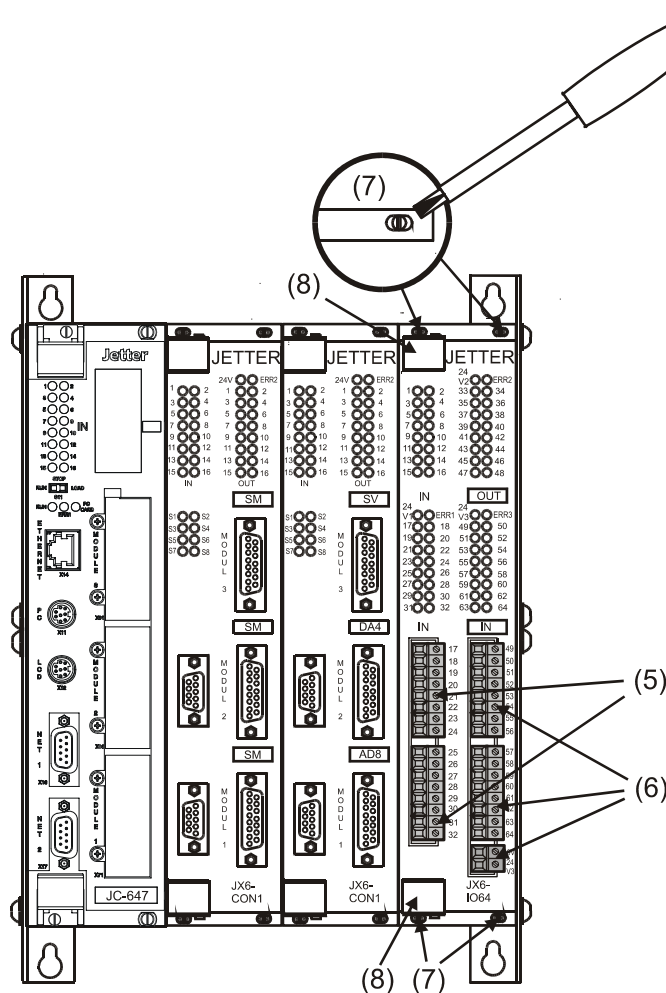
Frontansicht auf JX6-Gehäuse mit Modulen
